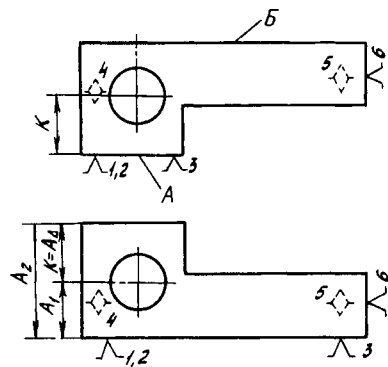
Дополнительные размерные связи при несовпадении технологической базы с поверхностью, от которой задан размер детали
